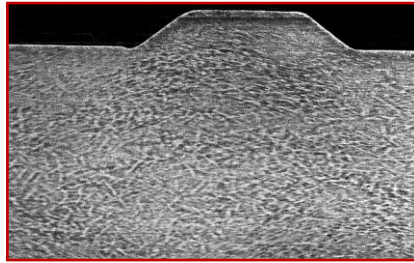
Вид зварного з'єднання сталі з феритною структурою
